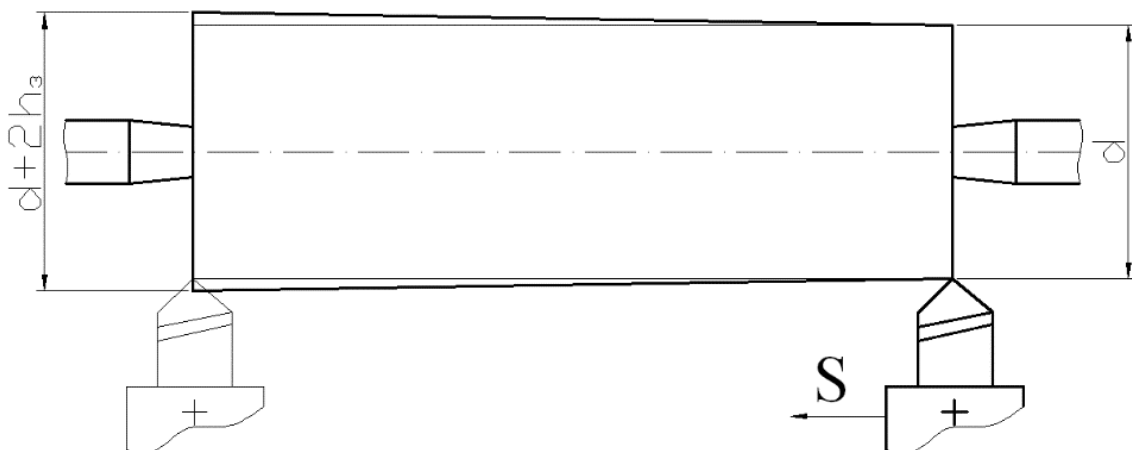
Схема влияния износа резца на размер обработанной поверхности
